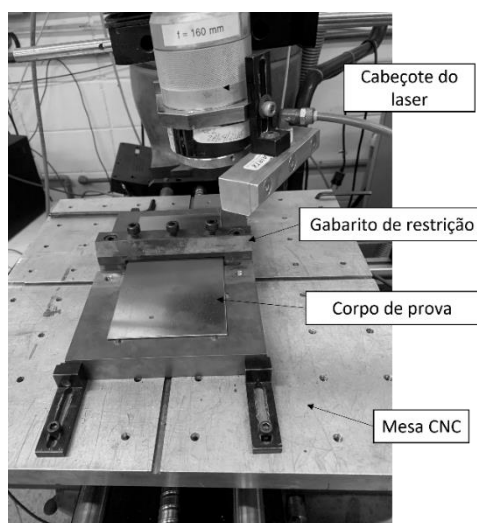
Conjunto cabeçote do laser e mesa de processo junto com detalhe da montagem da chapa na mesa de processo.
